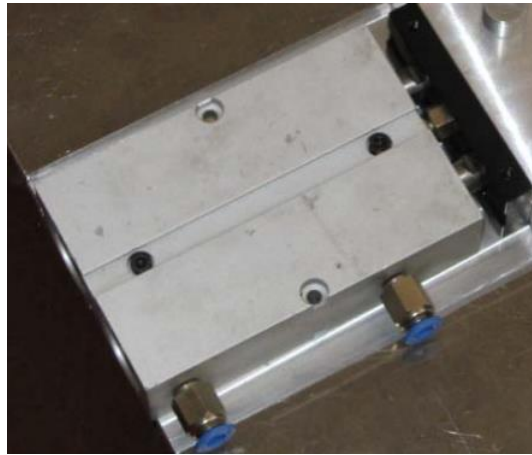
Вибраний пневматичний циліндр для лінійного руху упаковки
